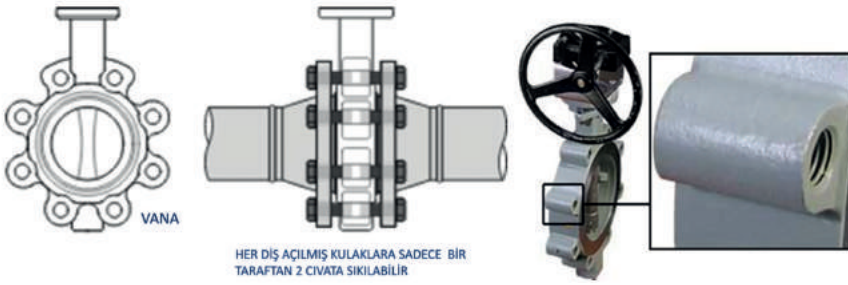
Flanşlı Vana- Boru Bağlantısı ve Conta
